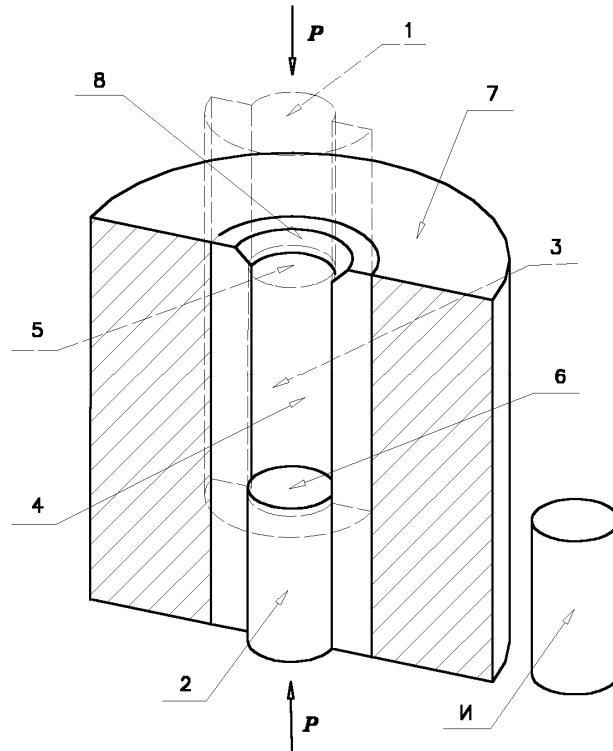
Пресс-форма для формования цилиндрической прессовки с двумя встречно-движущимися частями пассивной формообразующей поверхности
